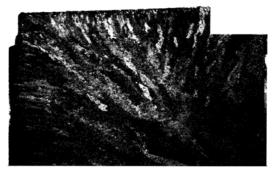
Макроструктура отливки вставки штампа для получения поковок вилки карданного вала (базовый вариант приготовления расплава)
